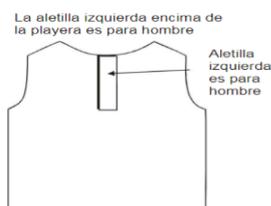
Colocar aletilla izquierda sobre la aletilla de la camiseta
